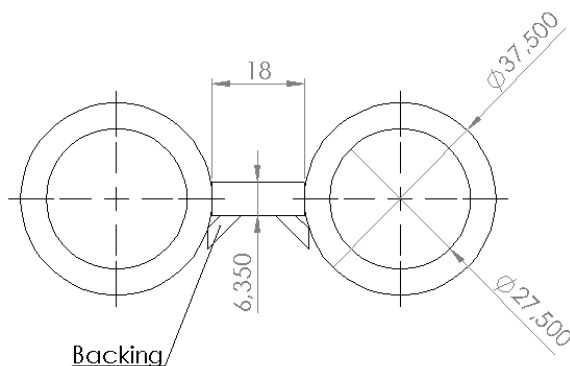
Design do corpo de prova para os ensaios de tubos e membranas.
